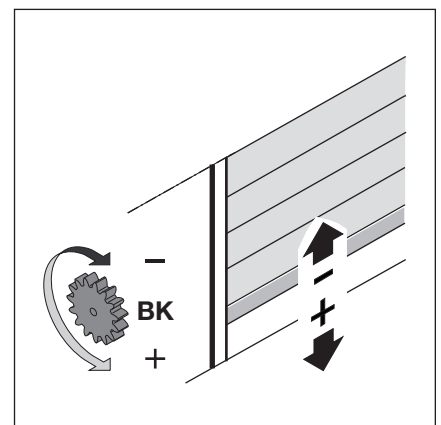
Винт с рифленной головкой для конечного положения *Ворота Закр.
